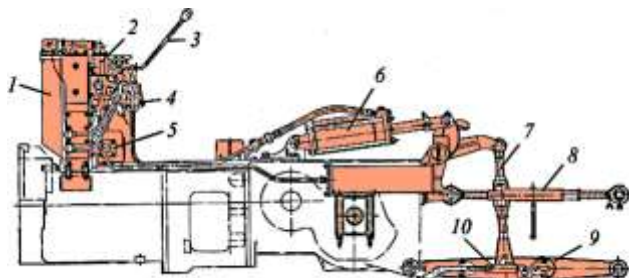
Гидронавесная система трактора МТЗ: 1 – корпус гидроагрегатов; 2 – распределитель; 3 - рукоятка управления распределителем; 4 – гидроувеличитель сцепного веса; 5 – насос; 6 – основной гидроцилиндр; 7 – раскосы нижних тяг; 8 – верхняя тяга; 9 – нижние тяги навески; 10 – муфта регулировочная
